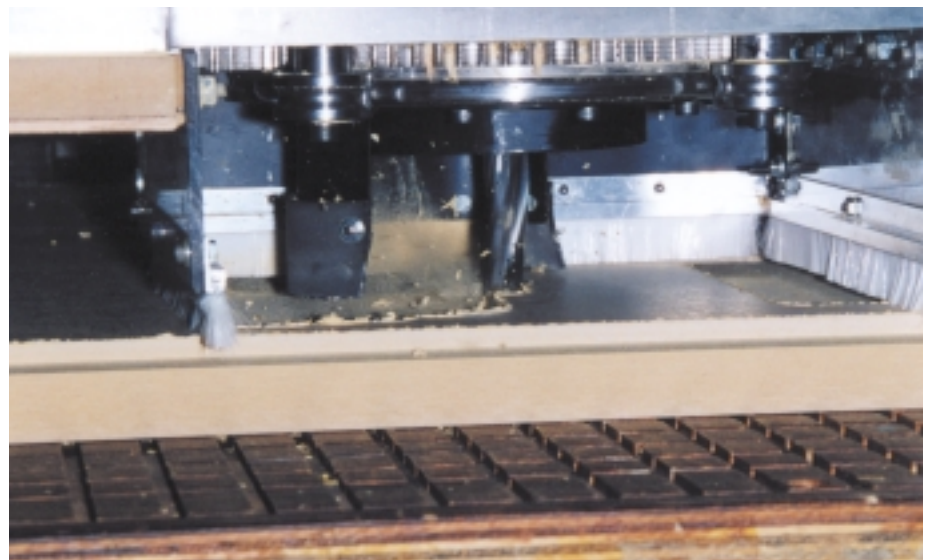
Détail du nouveau dispositif de captage - Detail of the new exhaust device
